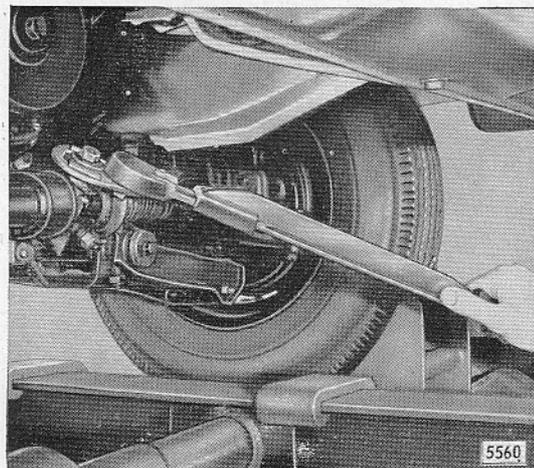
Stahlblech-Sechskantgegenmutter für Einstellschraube festziehen – im Bild Lenkgetriebe eingebaut
